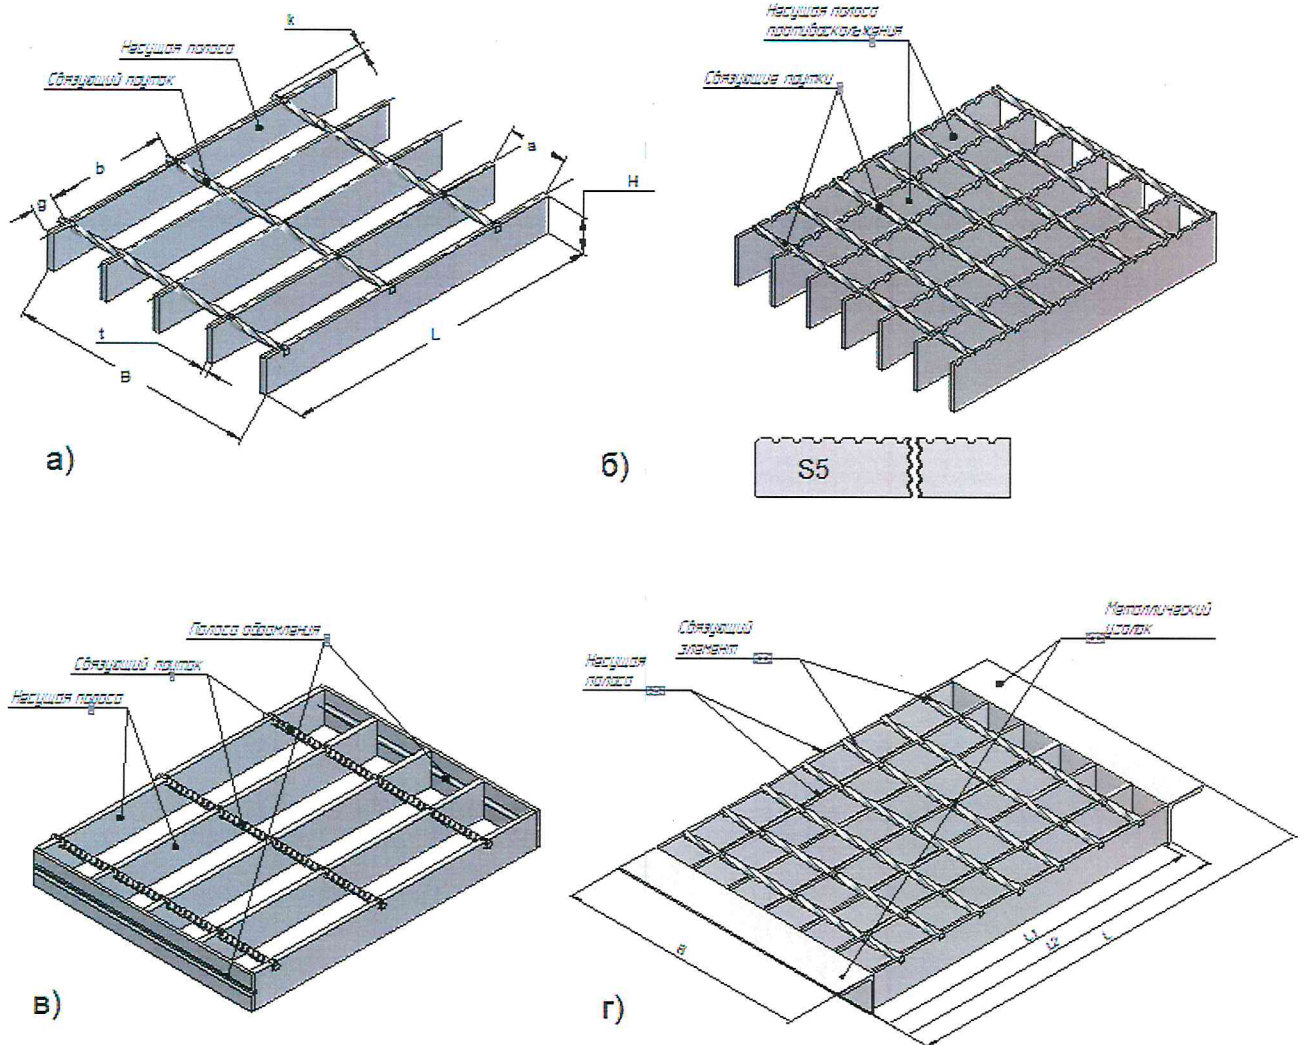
Типовой вид сварного настила: а) без обрамления со стандартной несущей полосой; б) без обрамления с полосой противоскольжения; в) с полосой обрамления; г) с уголком обрамления.
